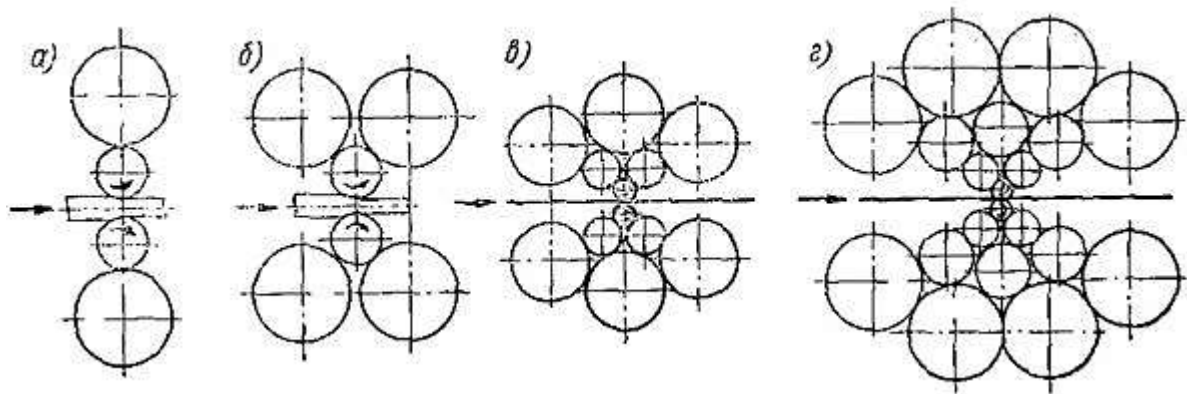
Схемы станов: а) кварто; б) шестивалкового; в) двенадцативалкового; г) двадцативалкового
